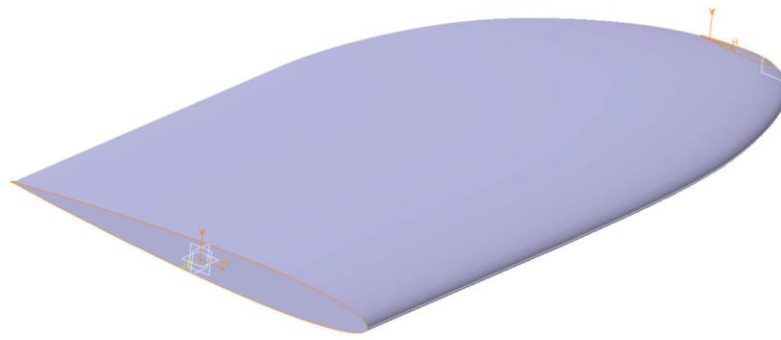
Multi-Sections Solid del estabilizador horizontal
